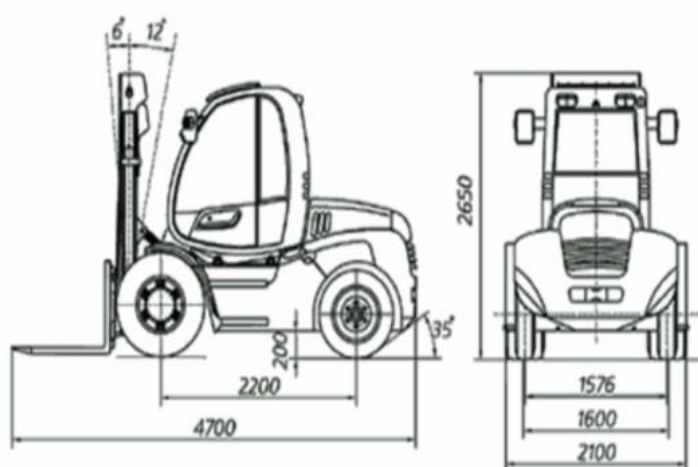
Габаритные размеры ТВЭКС ВП-05
